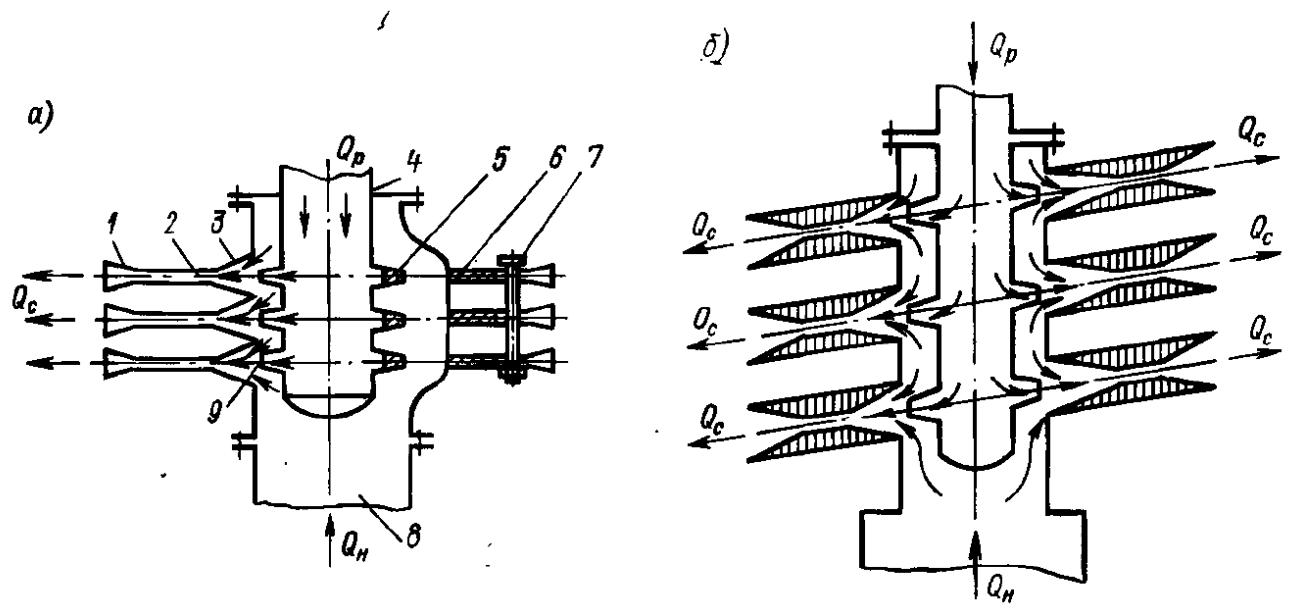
Схеми зблокованих струминних щілинних насосів [9]: а - а. с. 180290; б - по а. с. 800434; 1 – дифузор; 2 – камера змішування; 3 – конфузур; 4 – труба; 5 – сопло; 6 – камери змішування; 7 – болти; 8 – труба; 9 - сопло
